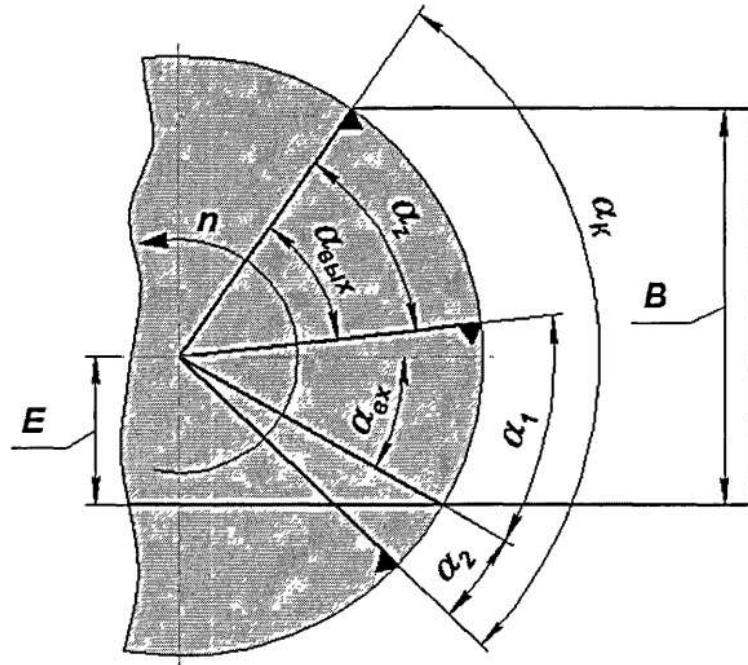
Геометрична схема розташування зубів фрези в процесі різання.
